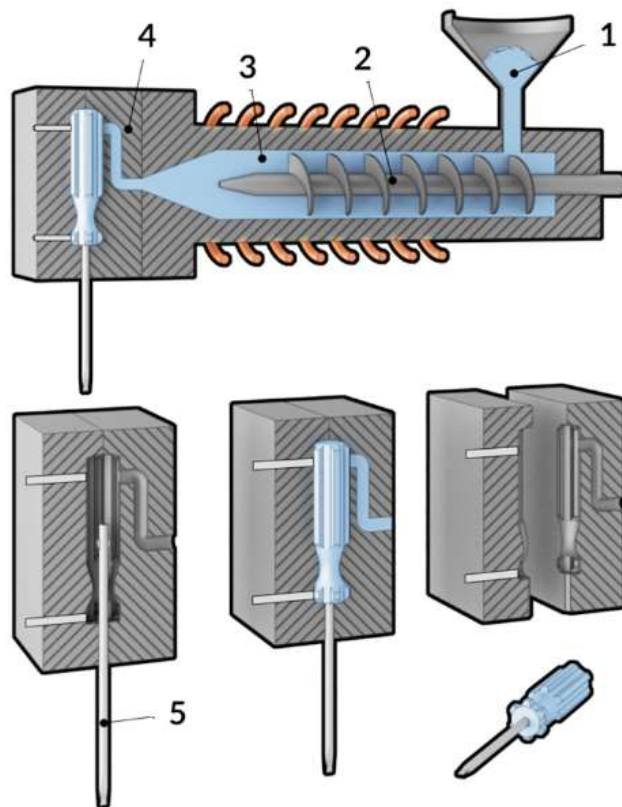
Схема виготовлення пластмасової ручки викрутки:
